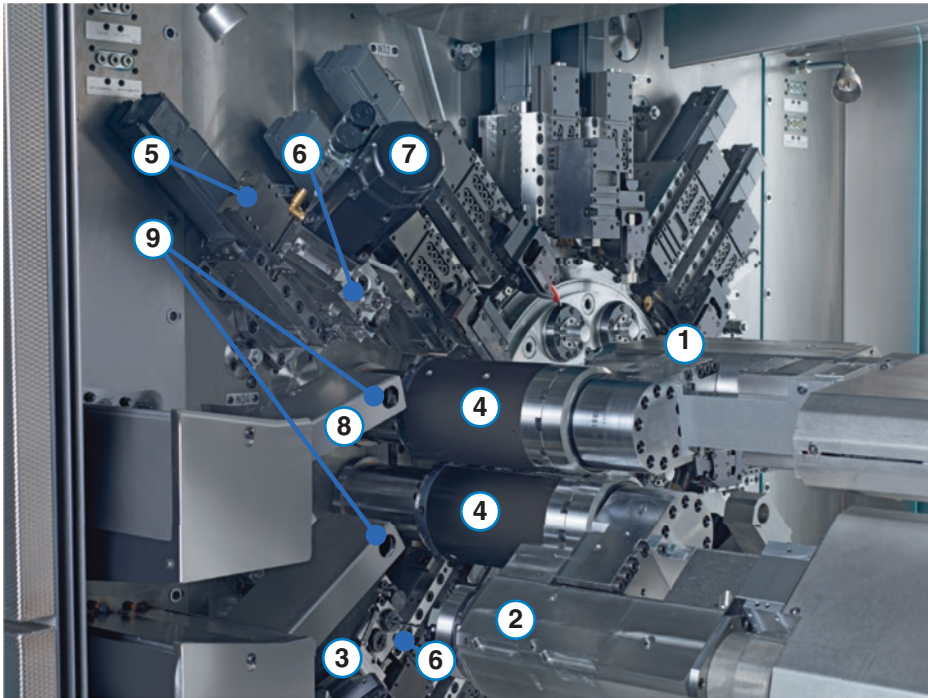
Arbeitsraum im Bereich der Rückseitenbearbeitung einer Maschine der Baureihe MS-C mit Doppel-Gegenspindel. [Bildquelle: Inde15a]
